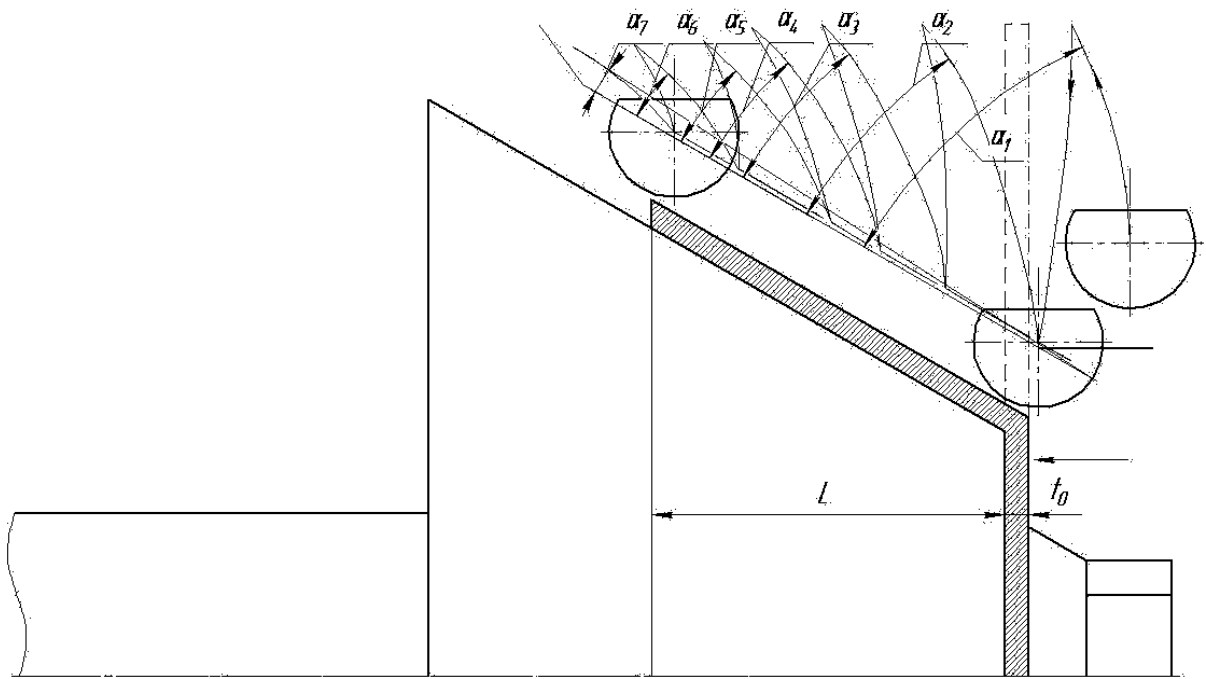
Траєкторії руху інструменту під час формування деталі ротаційною витяжкою
